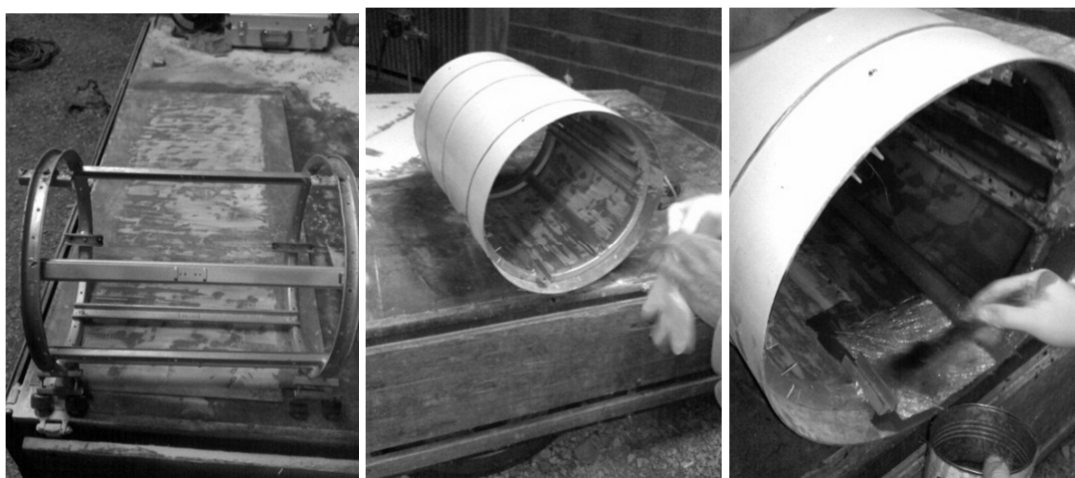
Etapas de Moldagem da fibra e fixação.
